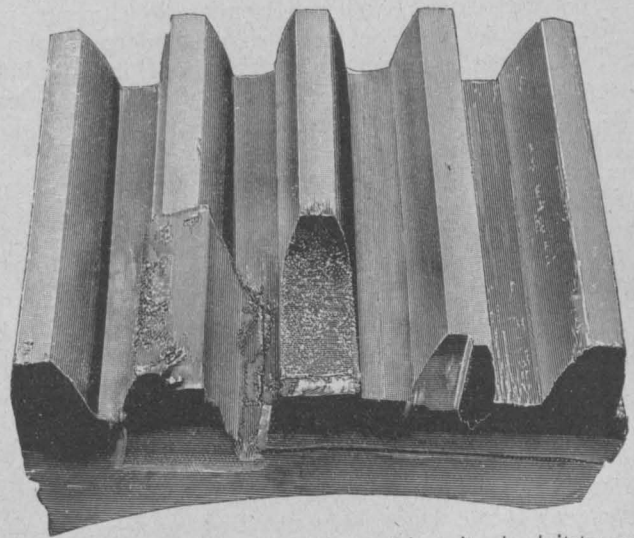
Zahnrad-Abschnitt mit abgebrochenem Zahn, mit unbearbeiteter und bearbeiteter Aufschweißung.
